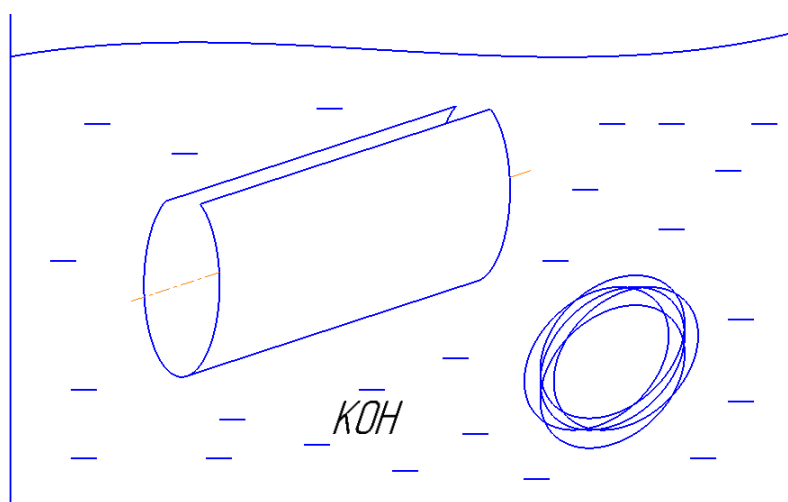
Эскиз операции травления заготовок и присадочной проволоки
